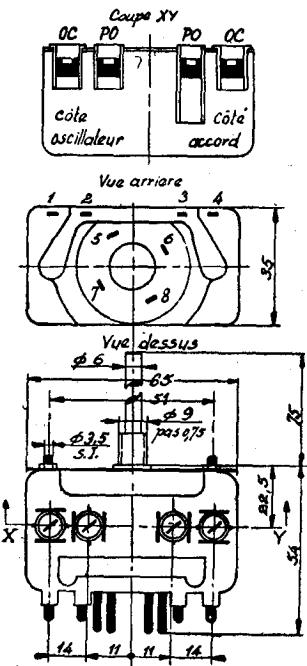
Aspect d'un bloc à 2 gammes : cotes d'encombrement et de perçage pour le châssis, vues arrière, de dessus et en coupe (Dauhin Oméga)
